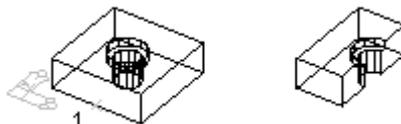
用于 ZOX 平面平行的平面作为剖切面
